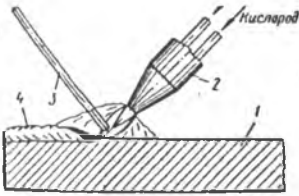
Схема газовой наплавки: 1 — наплаваемая деталь; 2 — газовая горелка; 3 — присадочный материал; 4 — плавящийся металл; 5 — толщина наплавленного металла
